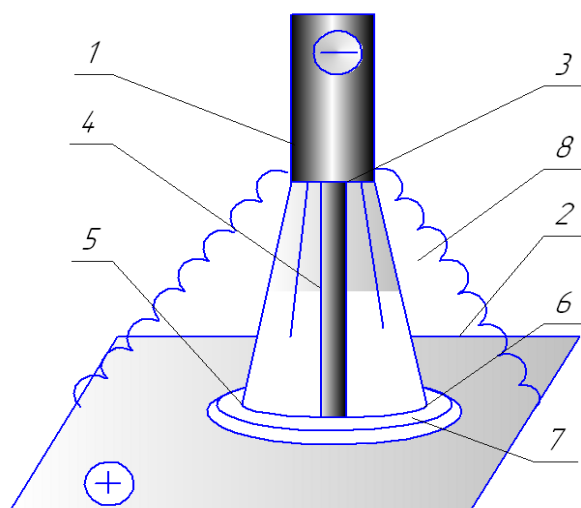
Принципиальная схема сварочной дуги:
